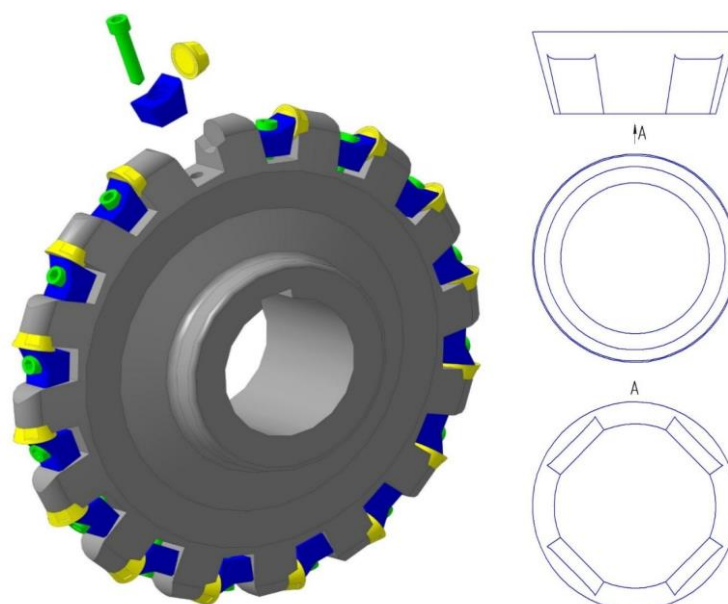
Разработанная конструкция сборной дисковой фрезы с круглыми пластинами с усечениями под паз гнезда корпуса фрезы
